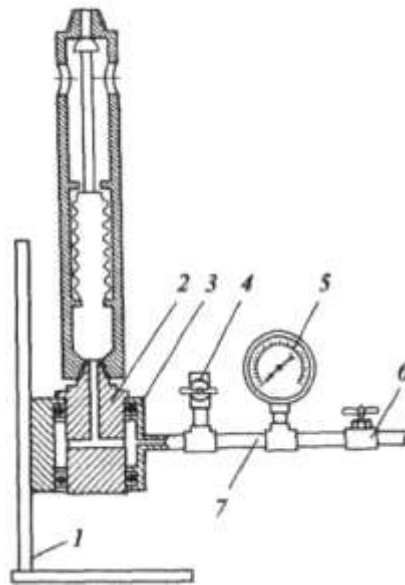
Стенд для зарядки і тарировки газліфтного клапана:
